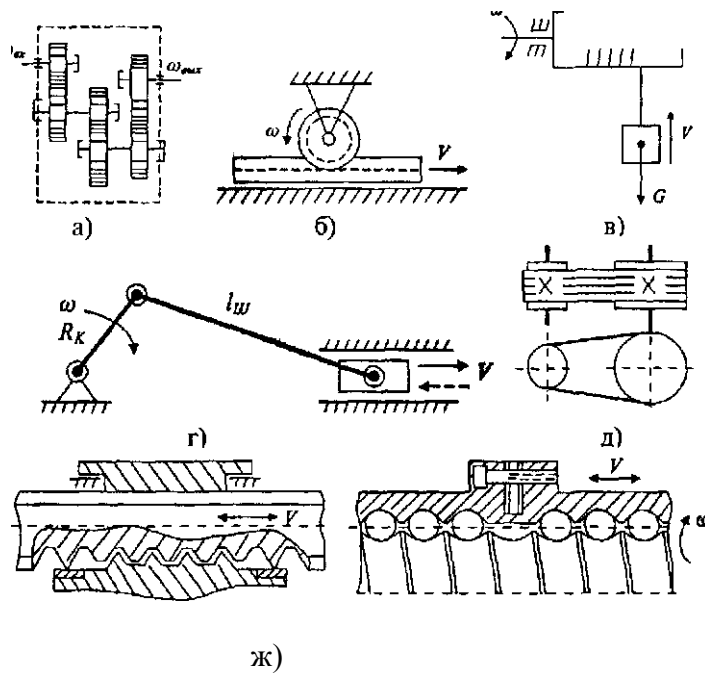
Механические передаточные устройства: а - редуктор; б - зубчатая передача; в - барабанно-канатная передача; г - кривошипно-шатунный механизм; д - ременная передача; е - винтовая передача; ж - шарико-винтовая передача
